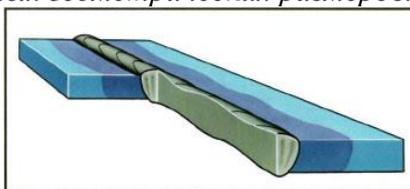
Нарушение формы сварного шва (Код дефекта: 500).
